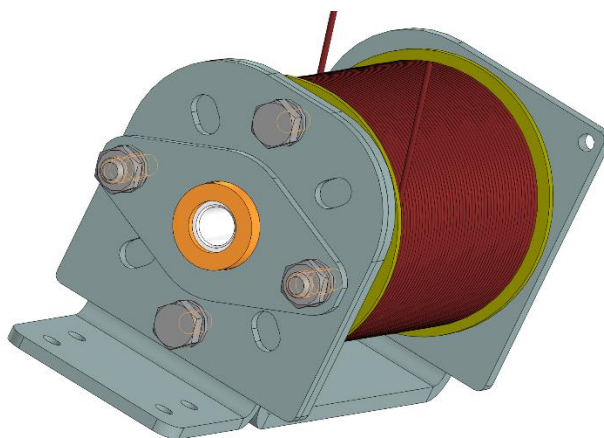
Установка прижимной ромбовидной шайбы 6.
